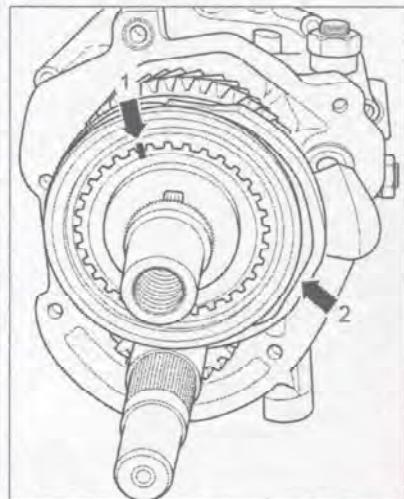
Отметьте положение для сборки скользящей муфты и ступицы синхронизатора 5-й/6-й передач (стрелка 1).
